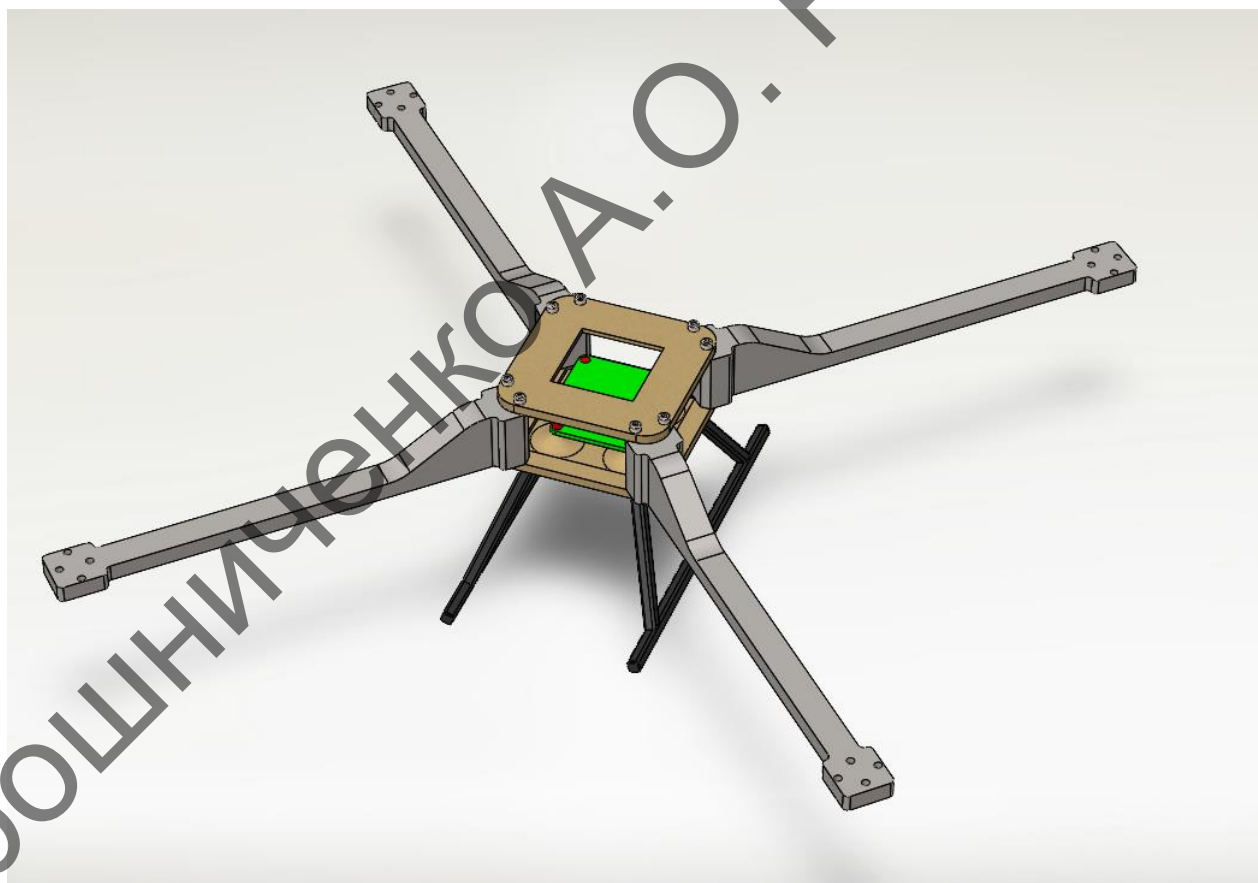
Корпус квадрокоптера в середовищі SolidWorks
